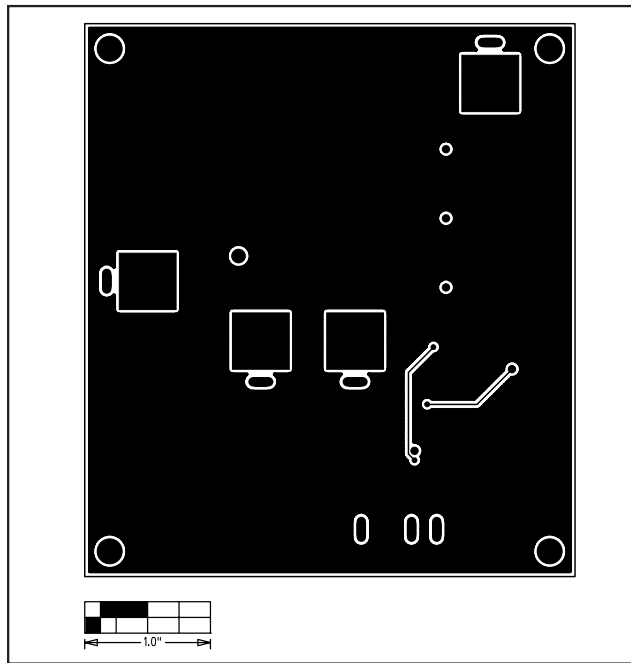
MAX5932 评估板 PCB 布局 — 焊接层
